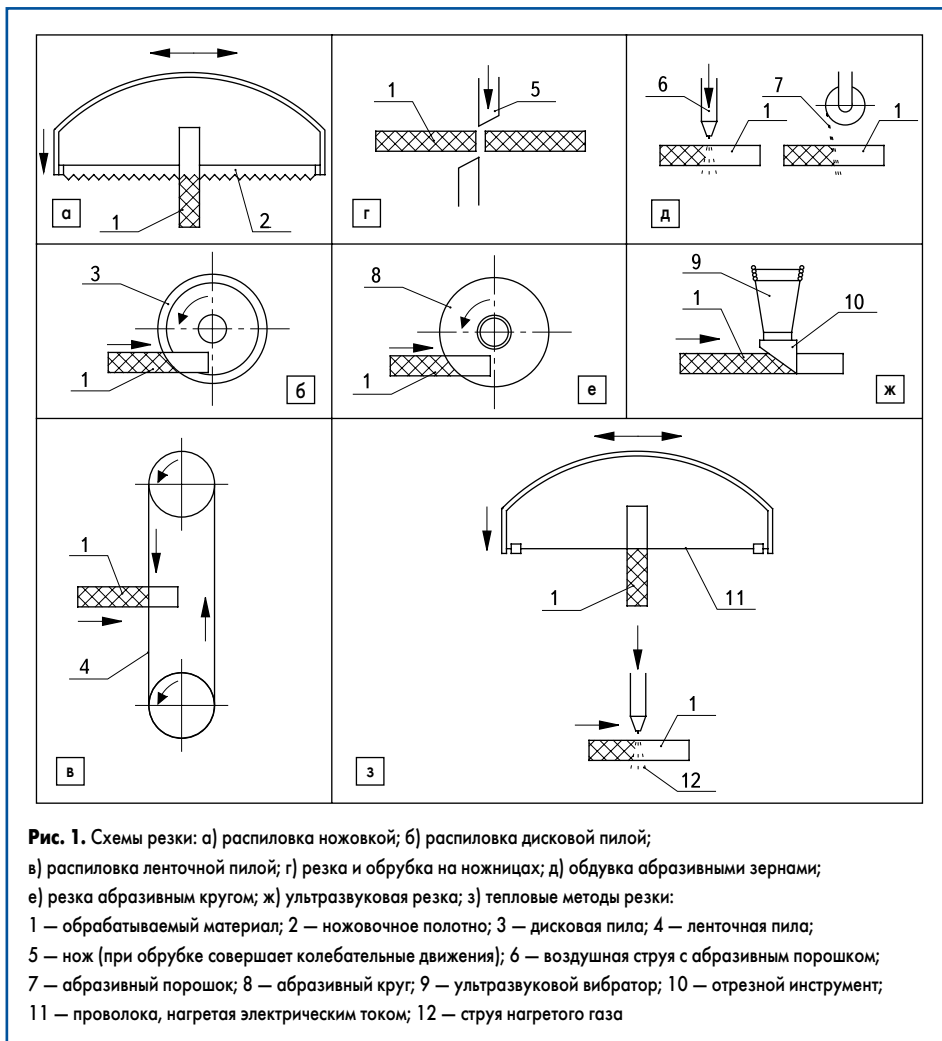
Схемы резки: а) распиловка ножовкой; б) распиловка дисковой пилой; в) распиловка ленточной пилой; г) резка и обрубка на ножницах; д) обдужка абразивными зёрнами; е) резка абразивным кругом; ж) ультразвуковая резка; з) тепловые методы резки: 1 — обрабатываемый материал; 2 — ножовочное полотно; 3 — дисковая пила; 4 — ленточная пила; 5 — нож (при обрубке совершает колебательные движения); 6 — воздушная струя с абразивным порошком; 7 — абразивный порошок; 8 — абразивный круг; 9 — ультразвуковой вибратор; 10 — отрезной инструмент; 11 — проволока, нагретая электрическим током; 12 — струя нагретого газа
